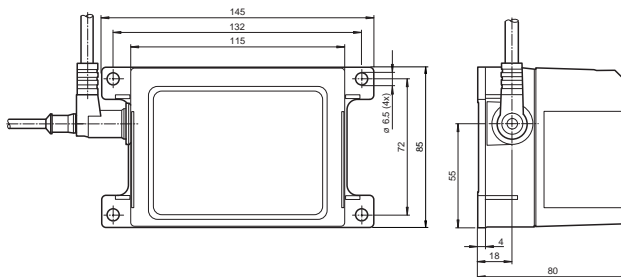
Abmessungszeichnung VDM54-6000-R/20/88/105 und VDM54-6000-R-3999
